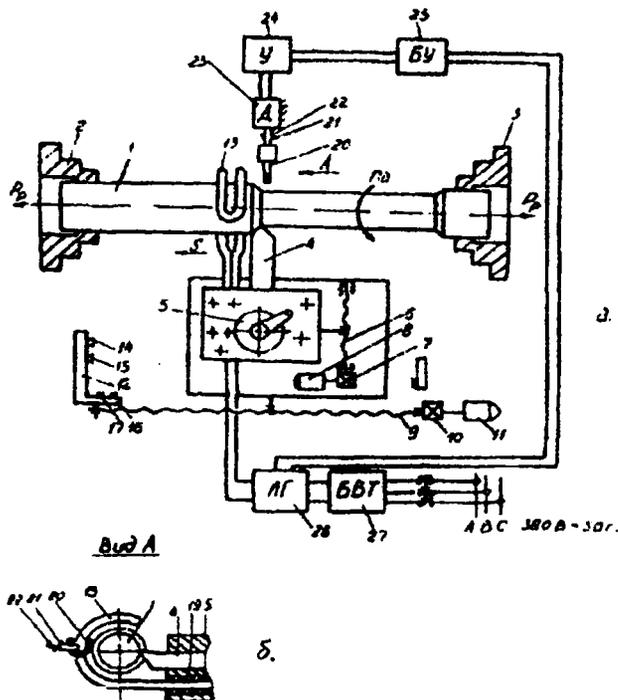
Устройство для реализации способа обработки нежестких деталей — тел вращения по а.с. N 1038072: а — кинематическая схема; б — вид по стрелке А.
